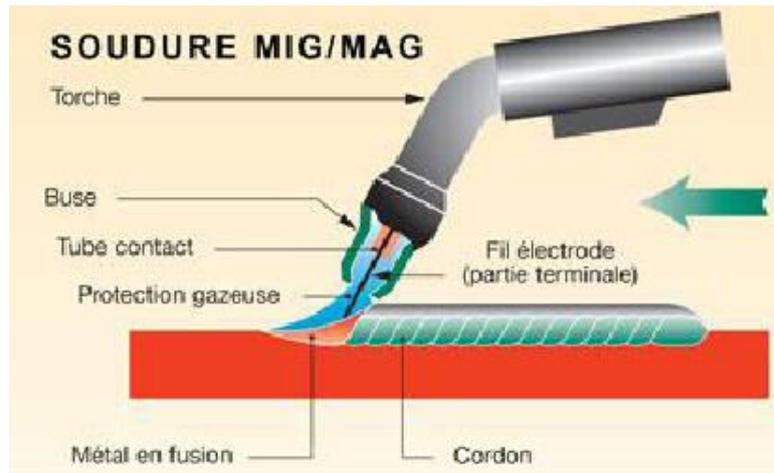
Principe de soudage MIG/MAG.
